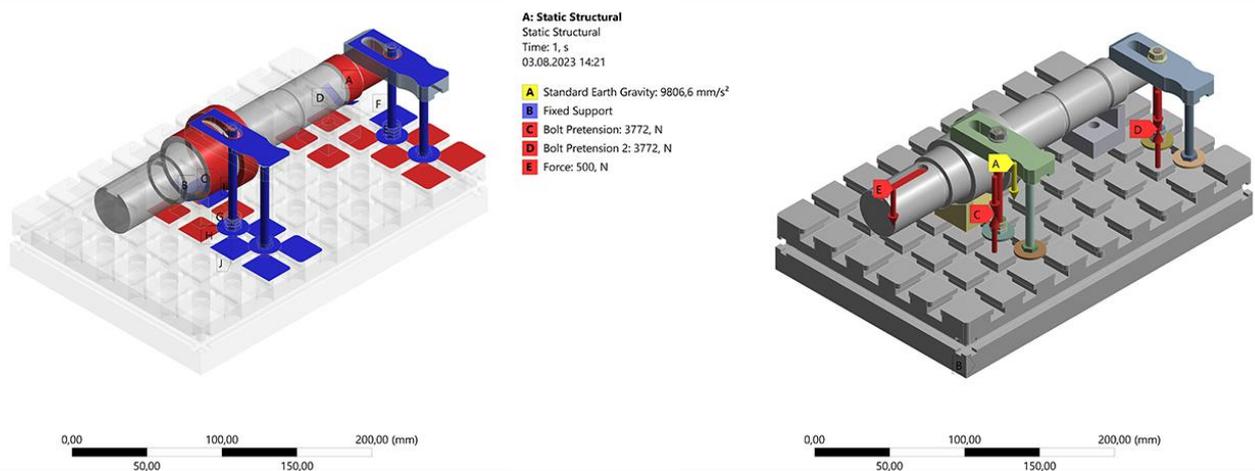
Контактные взаимодействия деталей станочного приспособления и приложенные закрепления и нагрузками
